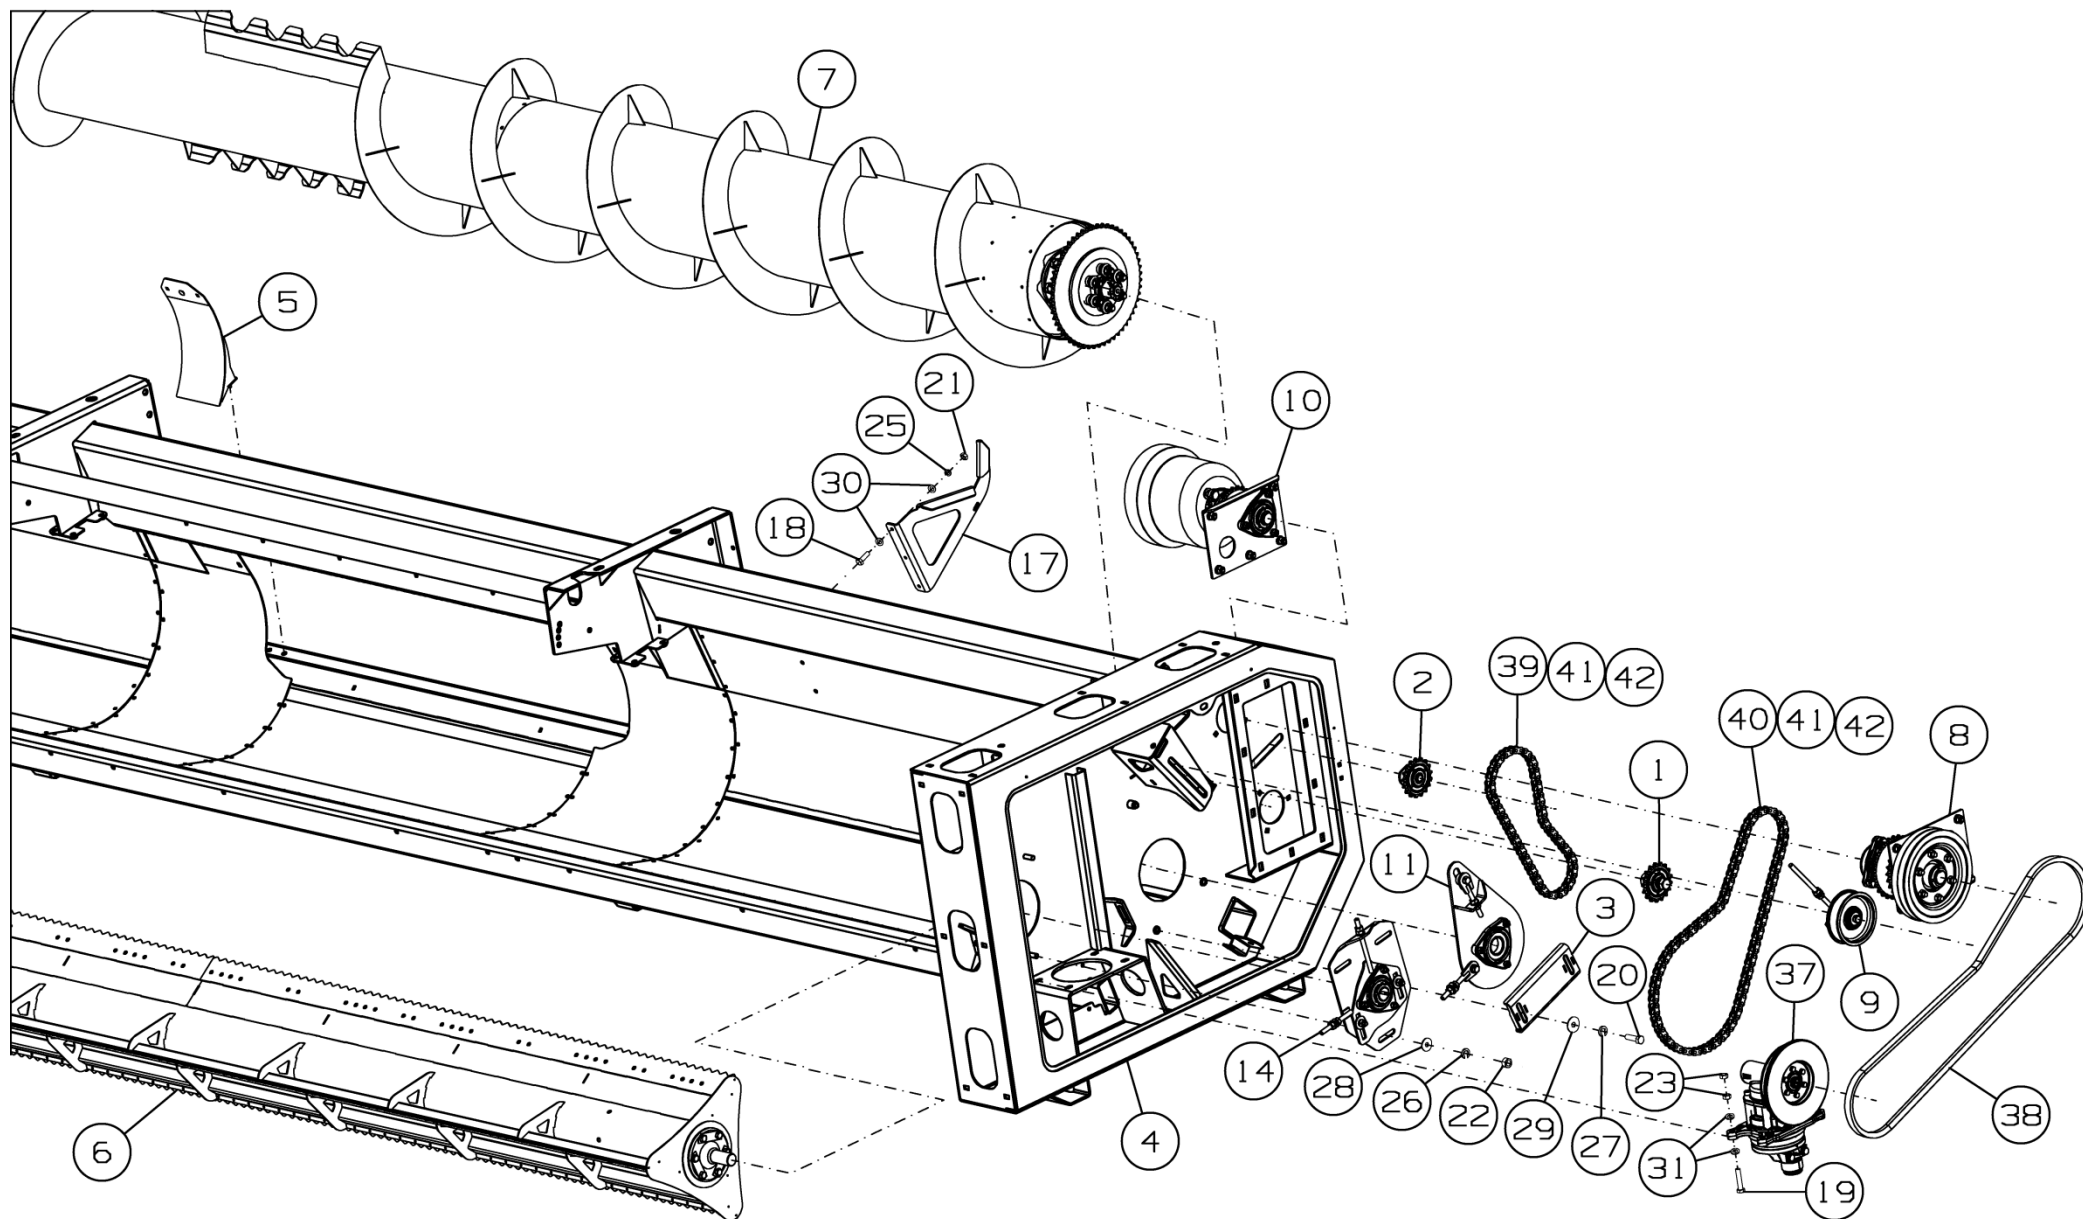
Корпус жатки SS-490.01.01.000-03 (левая сторона)
